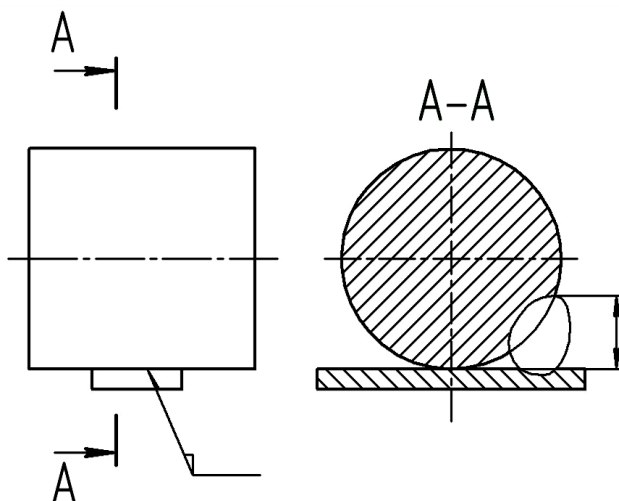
Изображение нестандартного сварного шва
